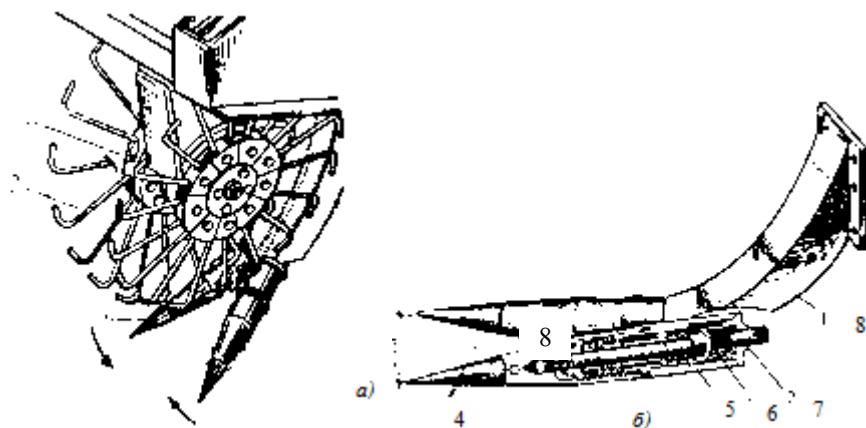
Ротаційно-вильчастий викопувальний робочий орган
